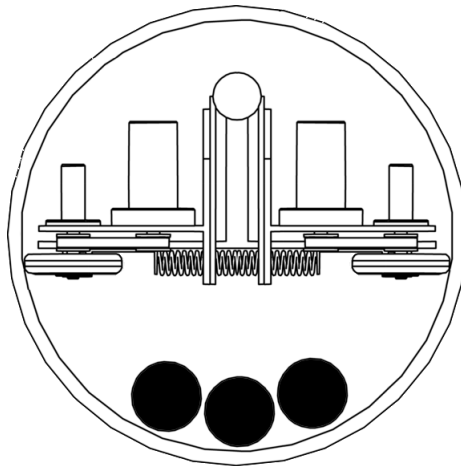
Posição em que o robô deve realizar a inspeção.
